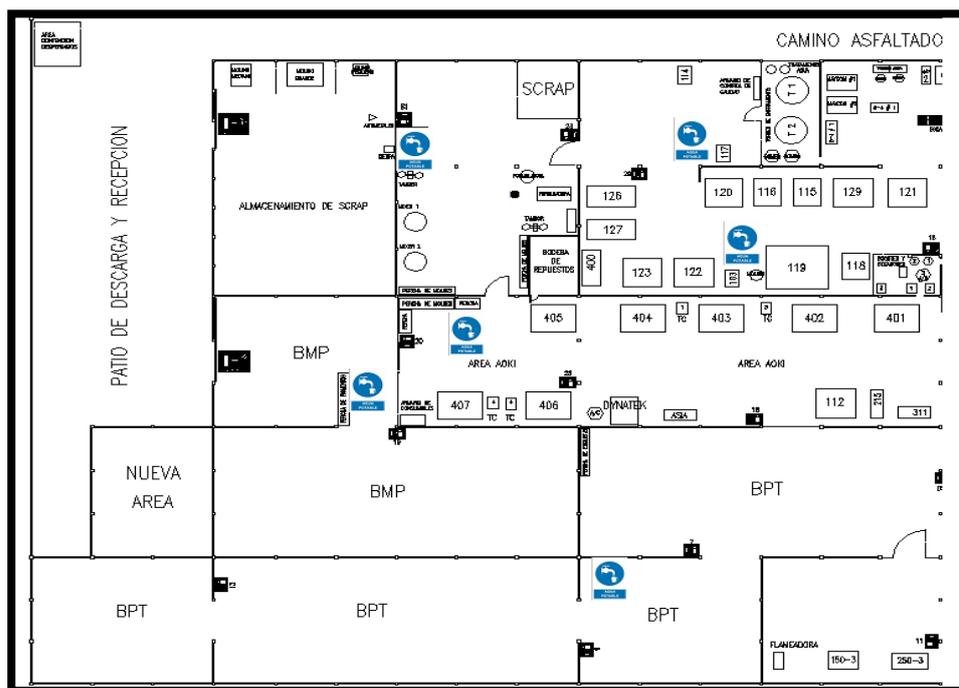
PUNTOS DE HIDRATACIÓN EN PLANTA 1
